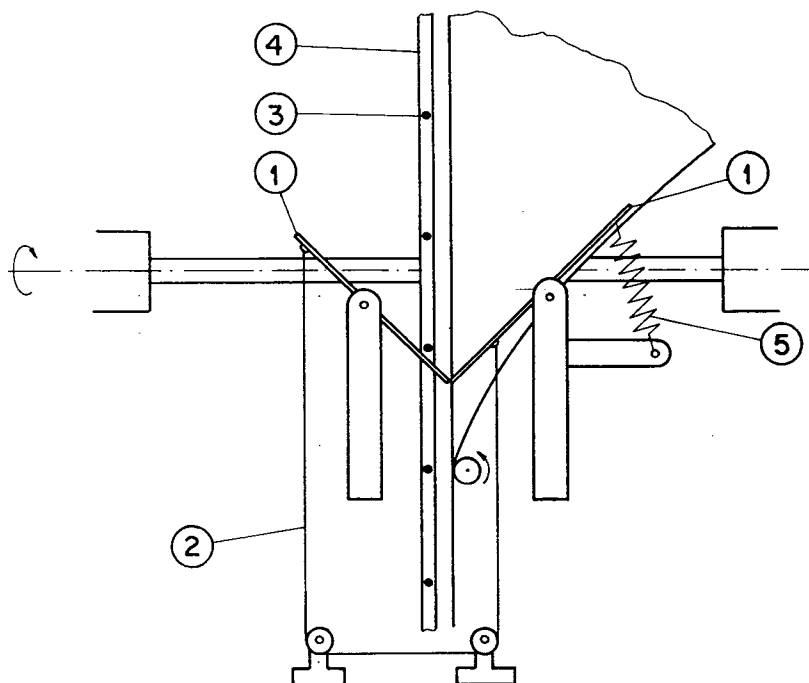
Vista frontal esquemática do dispositivo de dupla placa móvel.
